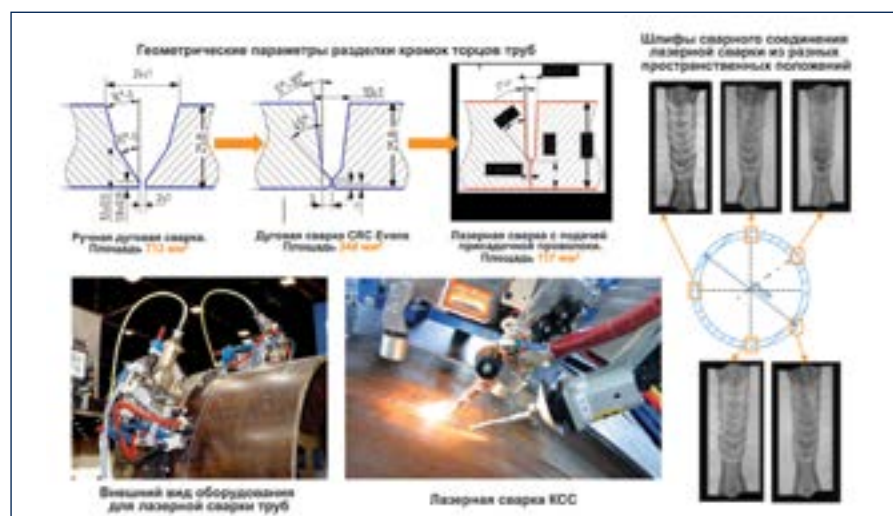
Лазерная сварка неповоротных кольцевых стыковых соединений труб
